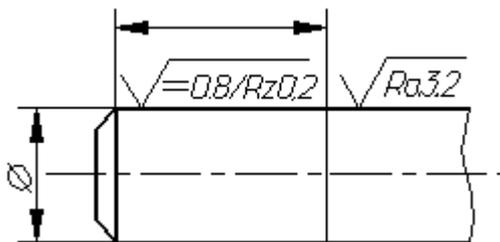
Пример обозначения различной шероховатости на одной поверхности
